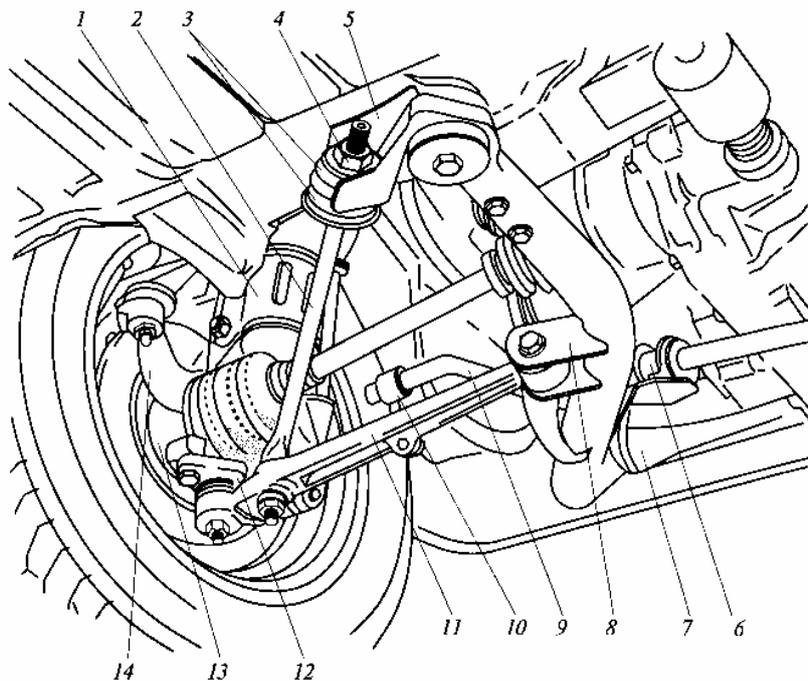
Подвеска левого переднего колеса: 1 — телескопическая стойка подвески; 2 — растяжка рычага; 3 — резиновые подушки растяжки; 4 — наружная гайка крепления растяжки; 5 — кронштейн крепления растяжки; 6 — кронштейн крепления штанги стабилизатора; 7 — подрамник; 8 — кронштейн крепления рычага подвески; 9 — штанга стабилизатора; 10 — стойка; 11 — рычаг подвески; 12 — шаровой шарнир; 13 — поворотный кулак; 14 — поворотный рычаг.
